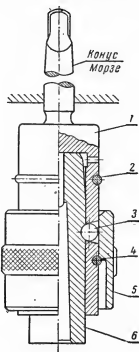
Патрон для быстрой смены режущего инструмента на сверлильном станке:
